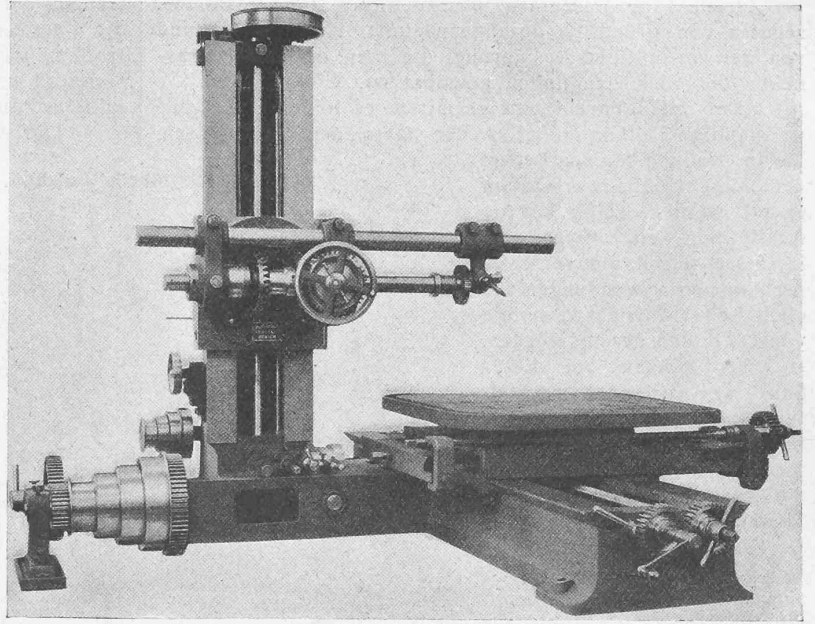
Universal-Fräsmaschine mit nach allen Richtungen selbstthätiger Schaltung.
